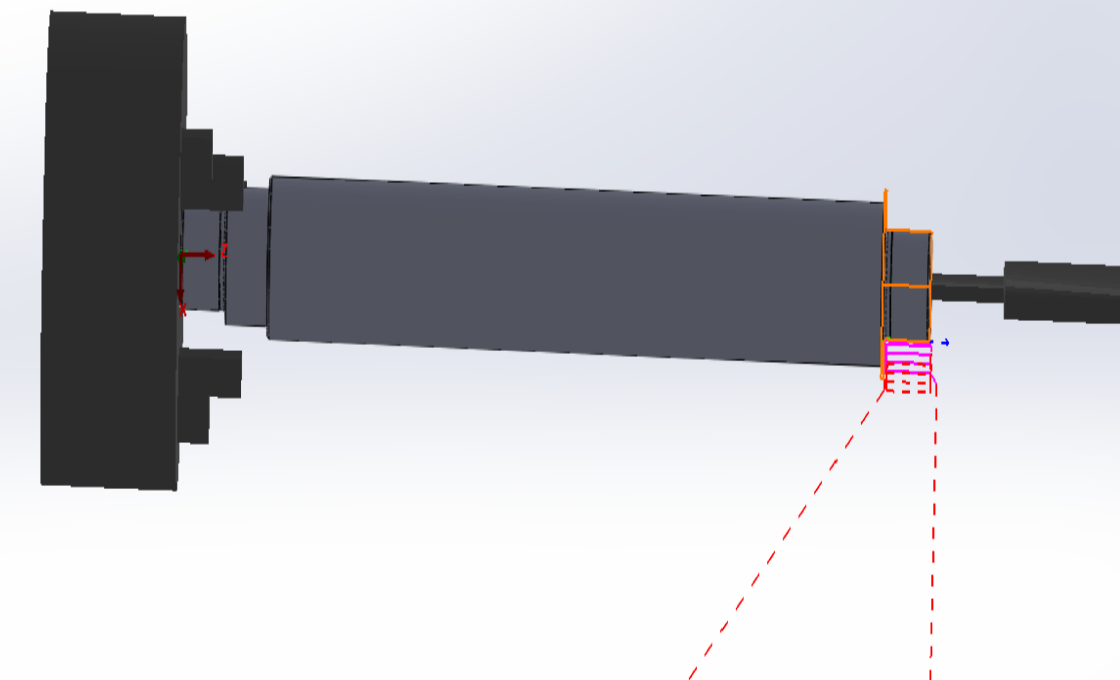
Чорнова та чистова обробка поверхні $\varnothing 35k6$
